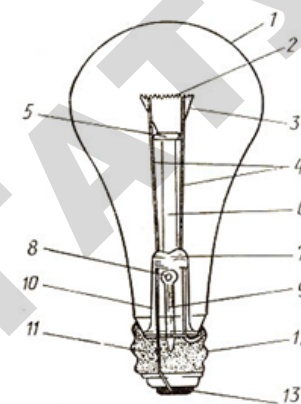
Устройство лампы накаливания: 1 — колба; 2 — тело накала; 3 — крючки-держатели; 4 — электроды; 5 — линза; 6 — штабик; 7 — лопаточка; 8 — откачное отверстие; 9 — штенгель; 10 — полый цилиндр; 11 — мастика; 12 — цоколь; 13 — контактная шайба
